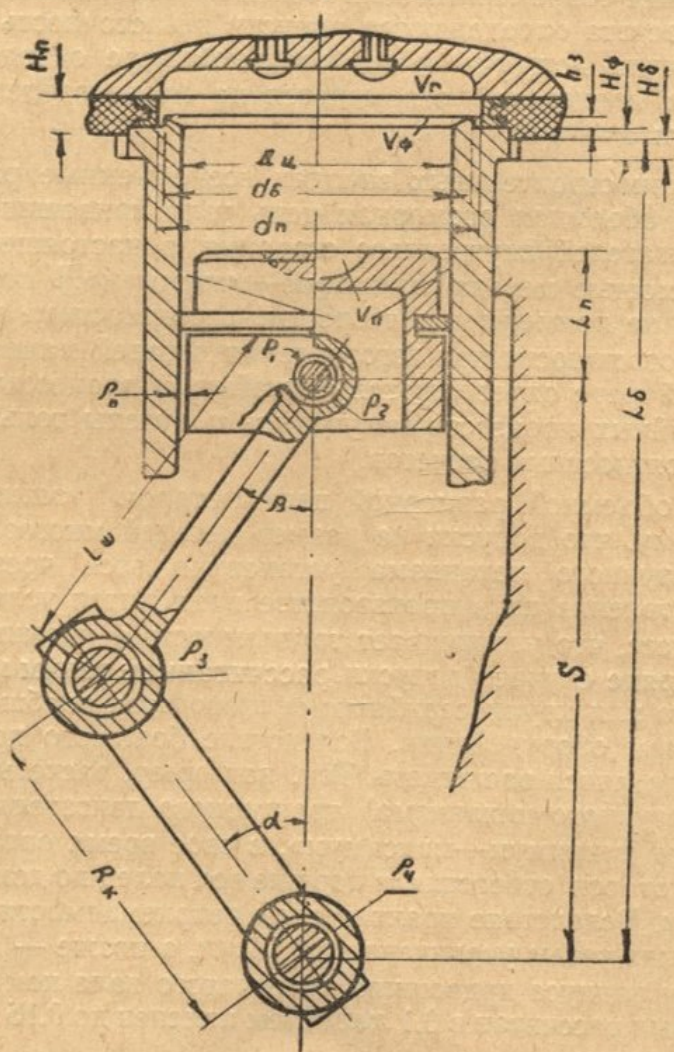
Типовая схема узла кривошипно-шатунного механизма рядного двигателя.
